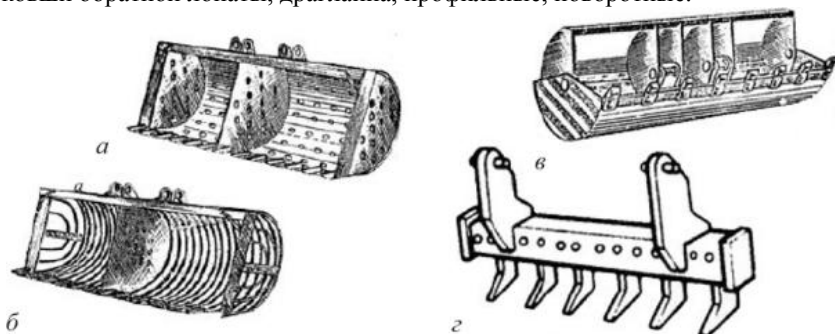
Виды сменных рабочих органов циклического действия: а — решетчатый ковш; б — решетчатый ковш с удлиненными зубьями; в — уширенный поворотный самоочищающийся ковш; г — корчующий рабочий орган.
